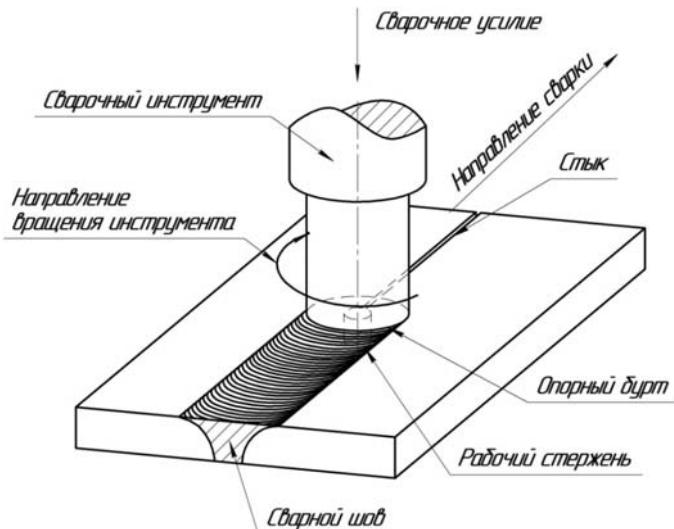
Схематичное изображение процесса фрикционной сварки [3]
